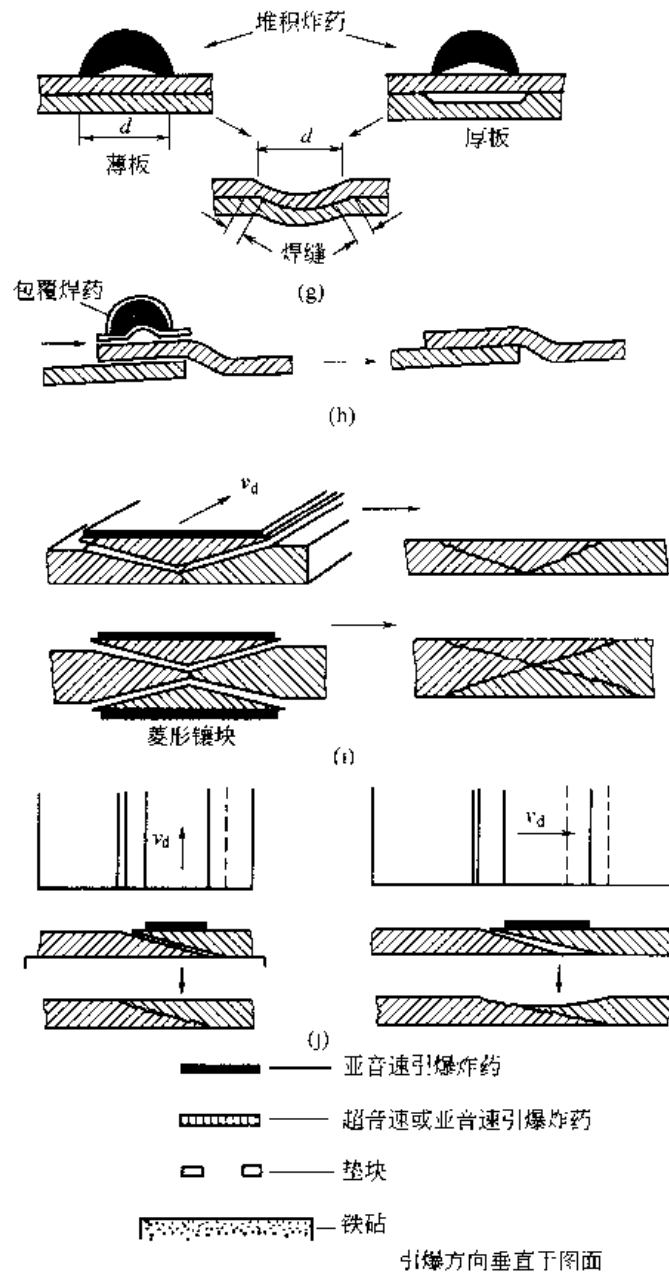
爆炸焊搭接和对接的接头形式
